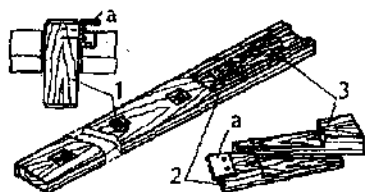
Вариант верстачной доски: 1 — гребенка; 2 — прижим; 3 — замок; а — стальной ерш (пластинка с зубцами)
